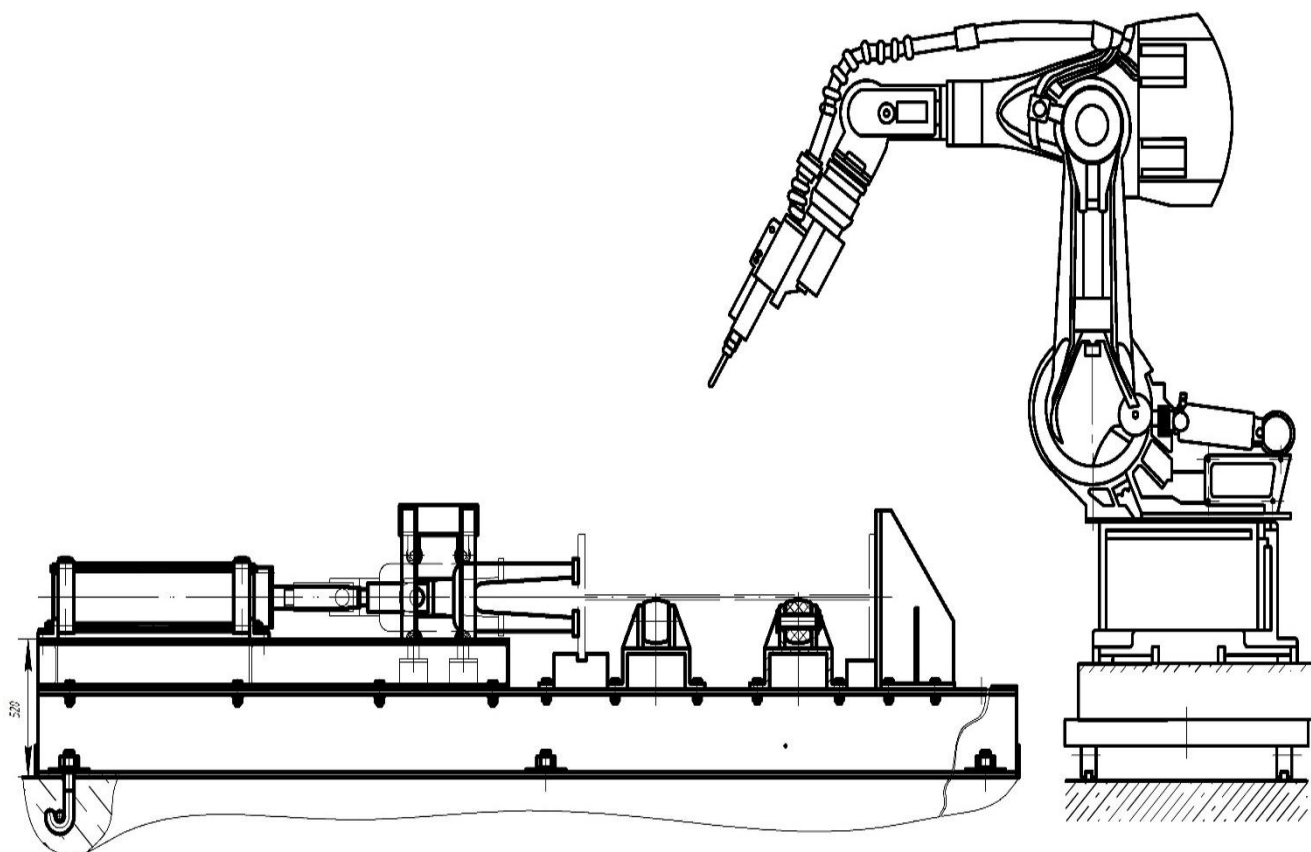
Стенд-установка виготовлення гофрбалки
